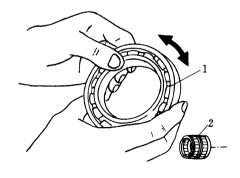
滚动轴承及滚针轴承的检查 1. 滚动轴承 2. 滚针轴承
